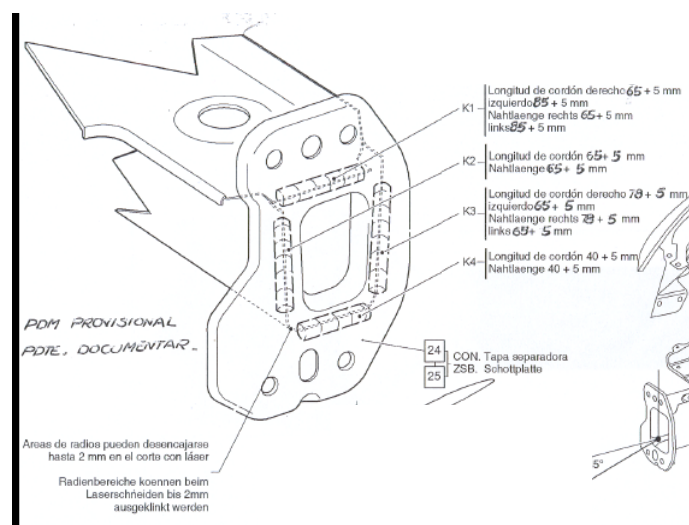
Cordones de soldadura realizados de forma automática
